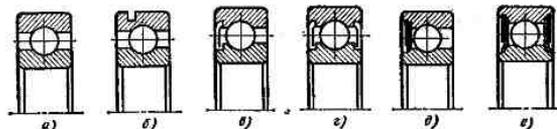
Шарикоподшипники радиальные однорядные типов: а — 0000; б — 5600; в — 6000; г — 8000; д — 16000; е — 18000
